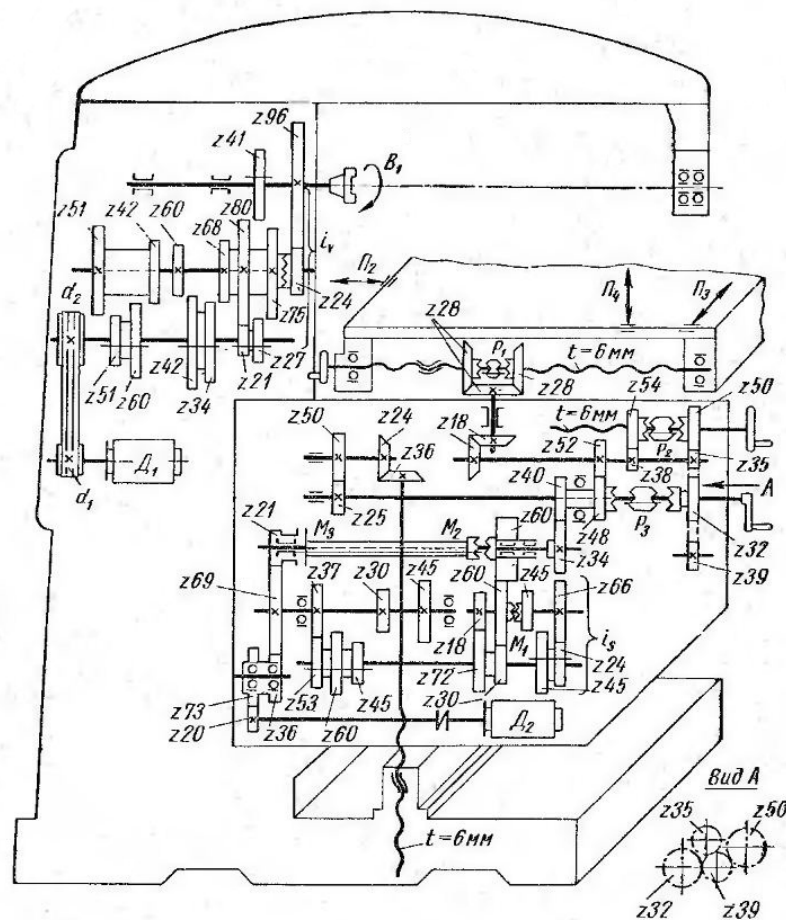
Кінематична схема універсально-фрезерного верстата 6Н80.
